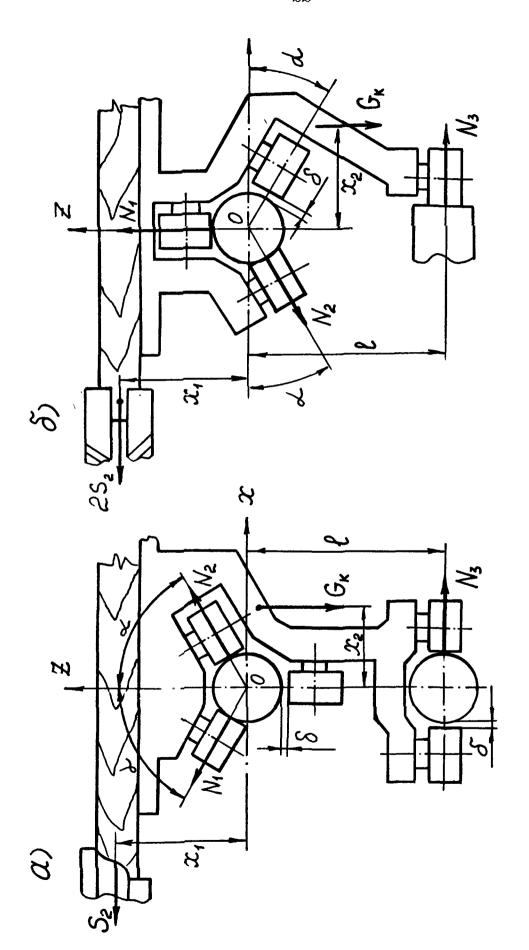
Расчетные схемы для определения реакций в опорах: а) фрезерного станка с шипорезной кареткой; б) шипорезного одностороннего станка
